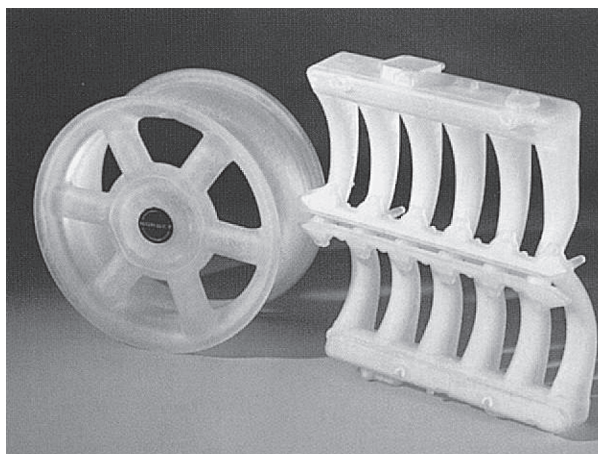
Prototype de jante en alliage d'aluminium et conduit d'admission moteur pour BMW.
